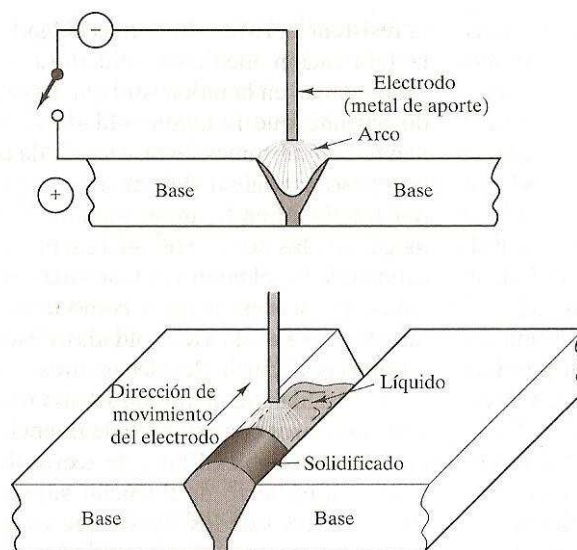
Esquema del procedimiento de soldadura por fusión.
